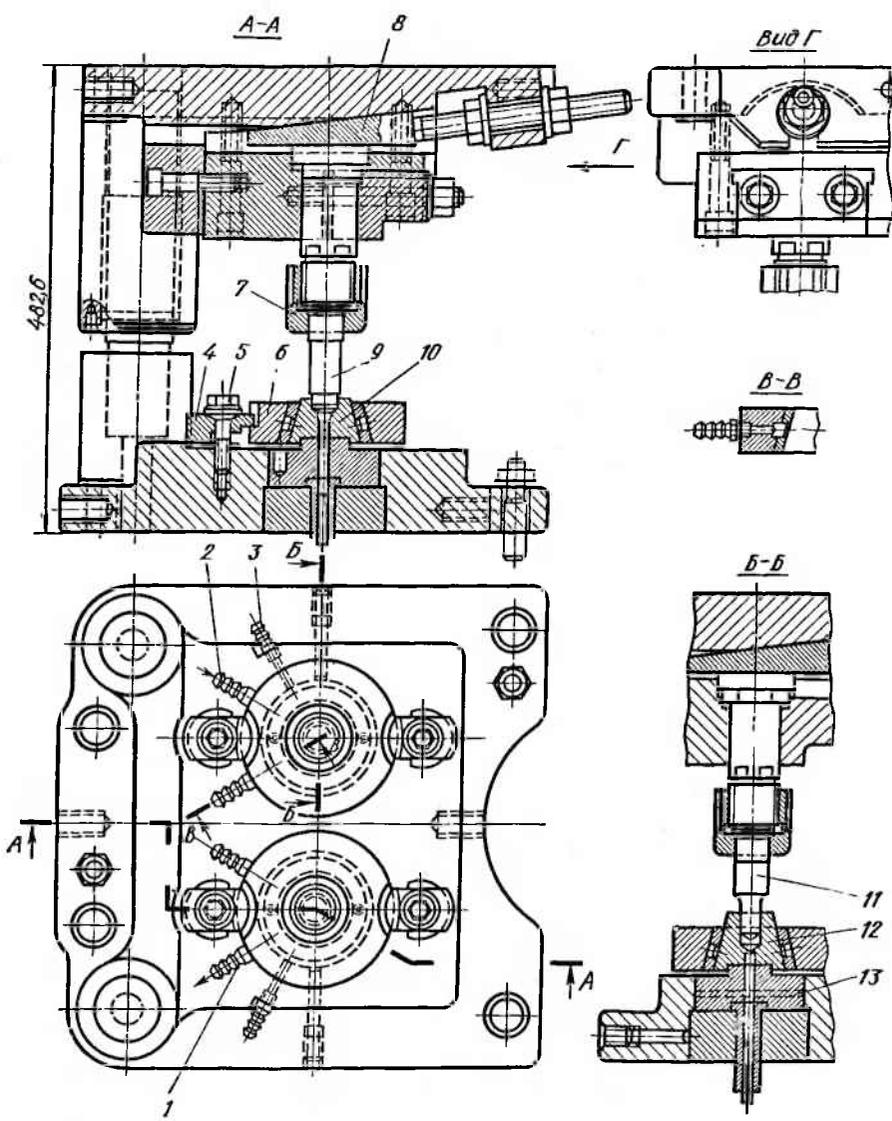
Штамп для изготовления поковок автомобильных клапанов
